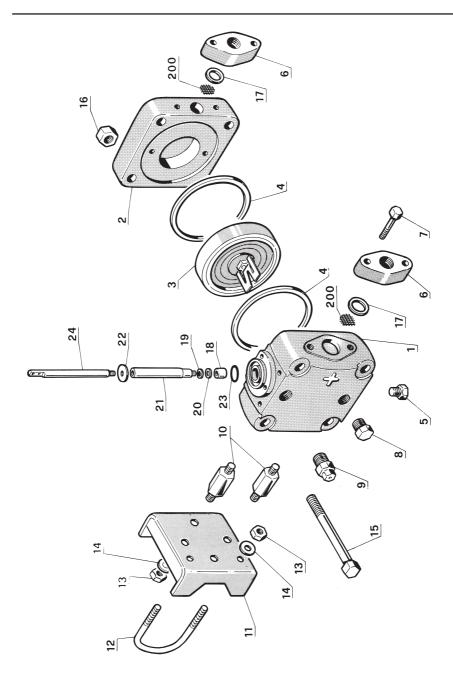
Vista esplosa del corpo e della capsula manometrica differenziale. Exploded view of body and of differential manometric capsule.
